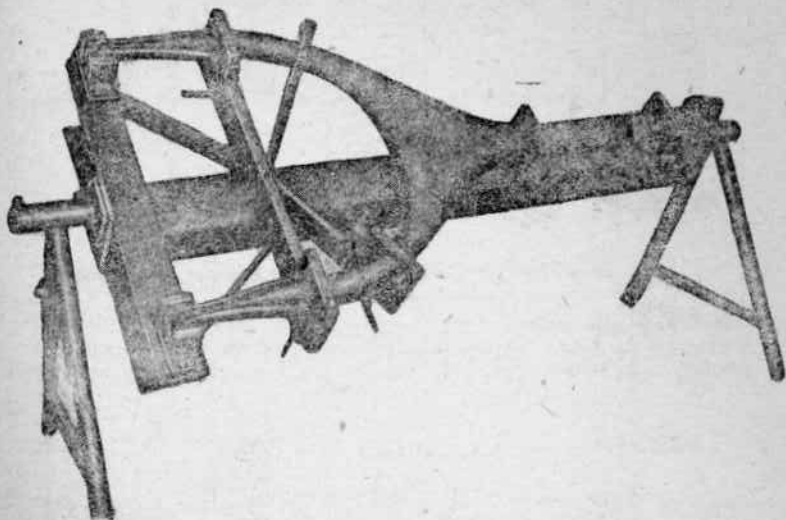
Приспособление для прихватки нижнего подкоса шасси.
